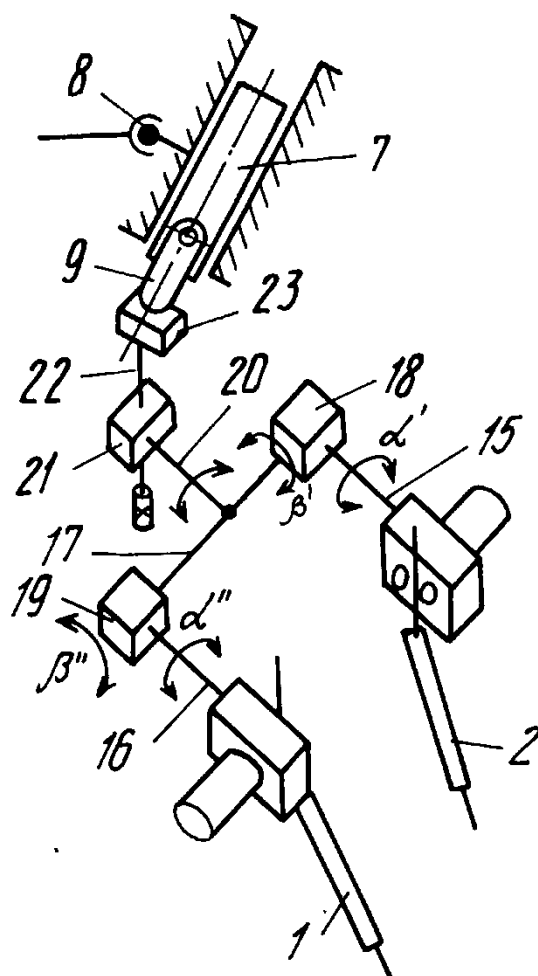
Кинематическая схема механизма регулировки положения наплавочных горелок
